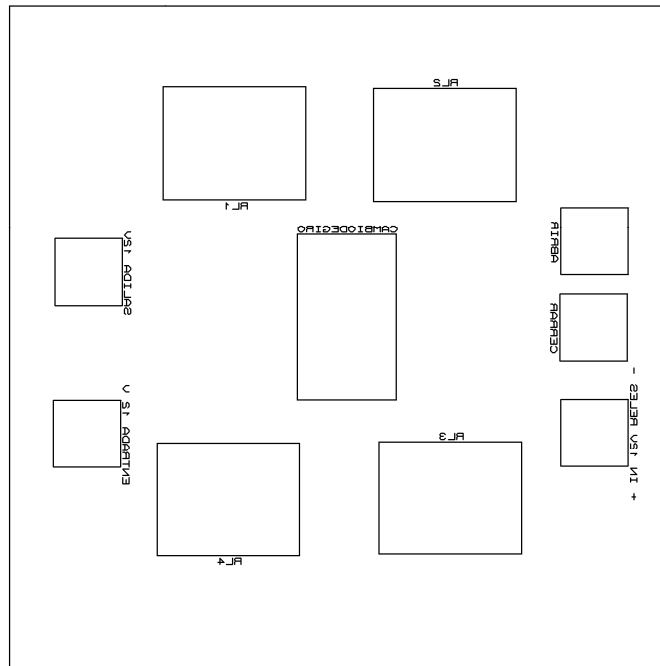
Top silk (Seda superior) Circuito inversor de giro de motor DC
